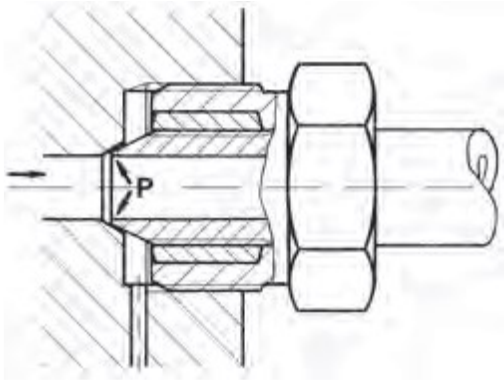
SITEC HP-Verschraubung bestehend aus Hochdruckrohr, Druckring und Druckschraube [2]
